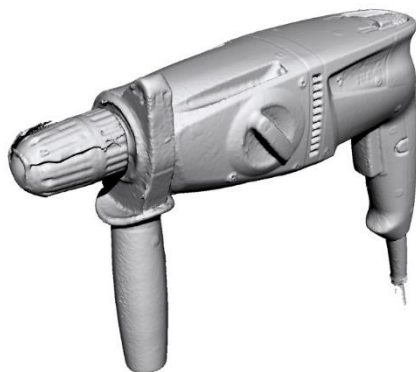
Vrtací kladivo – detail úchopu 2.
